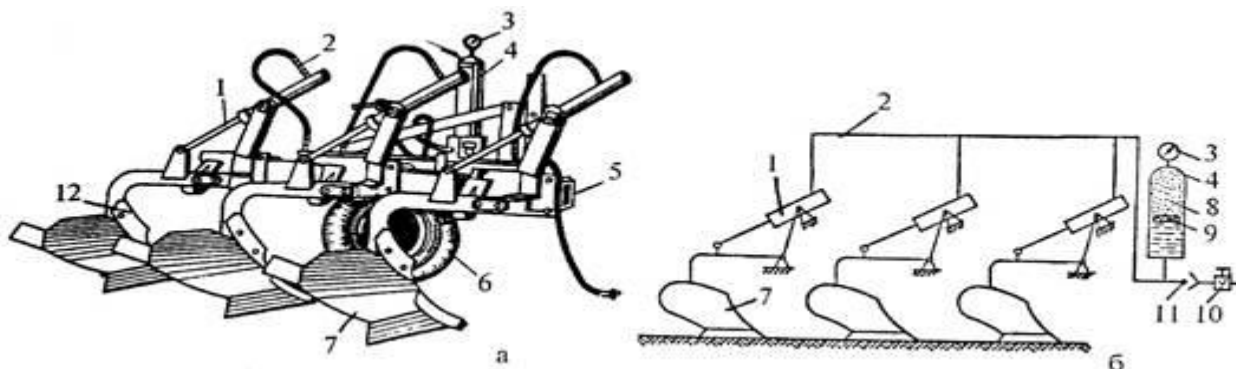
Начіпний плуг ПГП-3-40А (а) і схема гідропневматичногозапобіжного пристрою (б):
